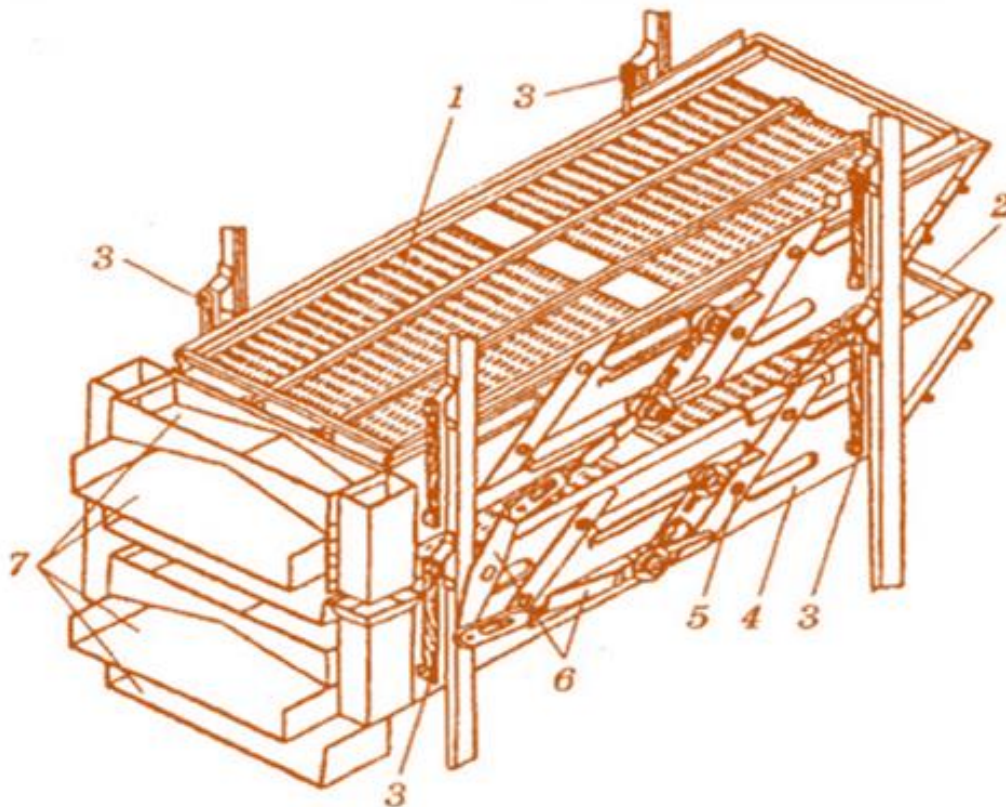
Решітні стани очисника вороху ОВС-25: 1 - верхній стан; 2 - нижній стан; 3 - пружина підвіски станів; 4 - боковина стана; 5 - ексцентриковий фіксатор; 6- механізм приводу щіток; 7 – лотоки.
